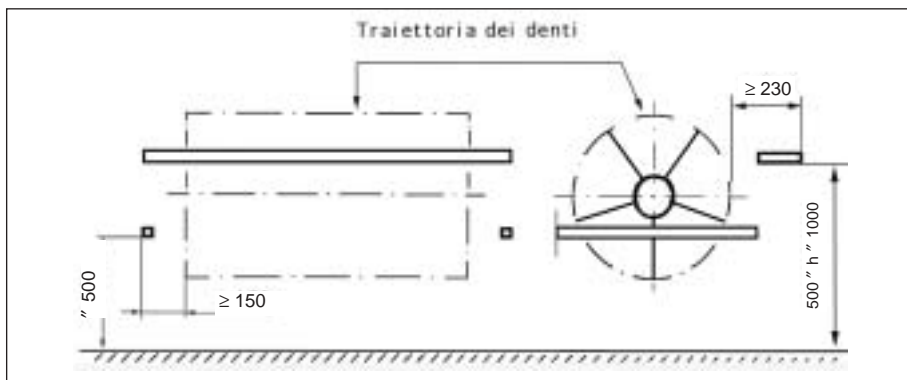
Vista frontale e laterale dei dispositivi di protezione (dimensioni in mm).
